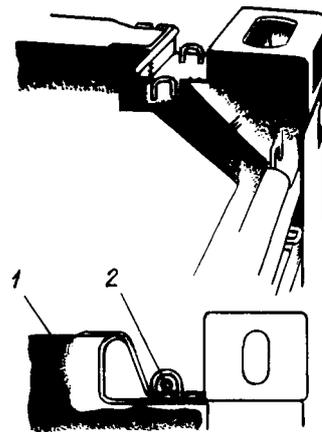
Устройство для крепления чехла к углам контейнера:
